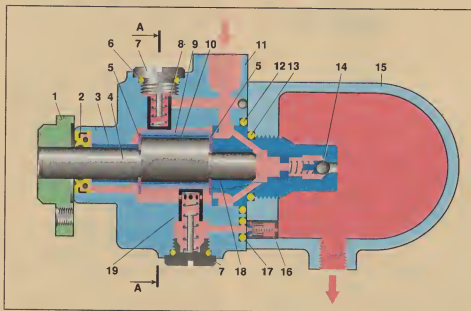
Схема гидронасоса ZF: 1 — ступица шкива; 2 — сальник; 3, 18 — втулки; 4 — эксцентриковый вал; 5 — шайба; 6, 12, 13, 17 — уплотнительные кольца; 7 — резьбовая пробка; 8 — плунжер системы тормозов; 9, 10 — втулки эксцентрика; 11 — корпус плунжеров; 14 — редукционный клапан; 15 — крышка; 16 — клапан; 19 — плунжер системы рулевого управления.
